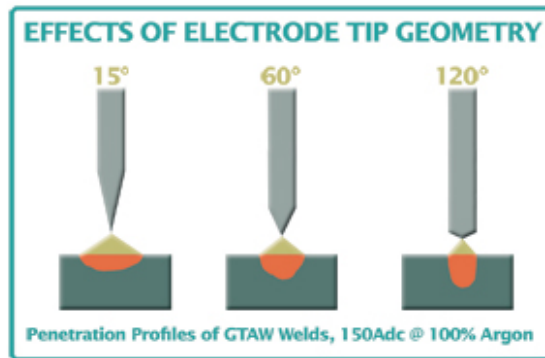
Penetración y anchura de cordón según la geometría de la punta del electrodo de tungsteno para soldadura TIG
